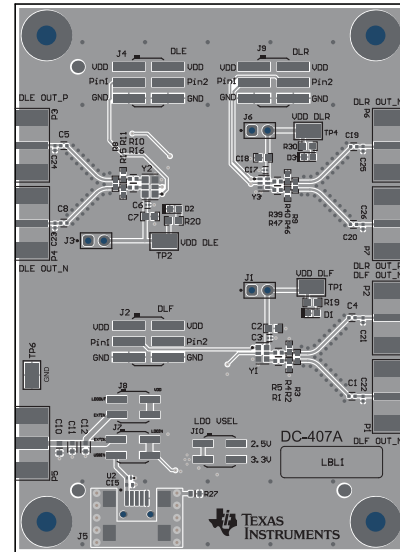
LMK6BEVM の PCB レイアウト例 - 最上層
